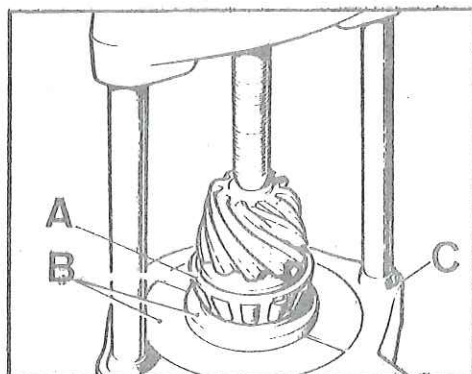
Montaje del cojinete de cabeza del piñón de ataque
